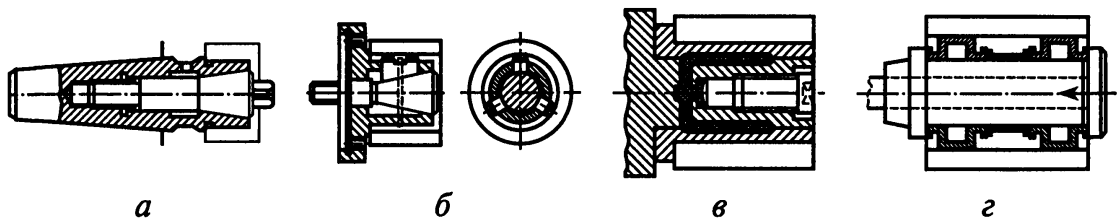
Разжимные оправки: *а* — консольная, с прорезями на рабочей шейке, служит для закрепления детали затяжкой внутреннего конуса; *б* — консольная, с тремя сухарями, разжимным внутренним конусом, используется для закрепления толстостенных деталей с обработанными или необработанными отверстиями; *в* — с упругой гильзой, разжимаемой изнутри гидропластмассой; *г* — с гофрированными втулками, обеспечивающая точность центрования
